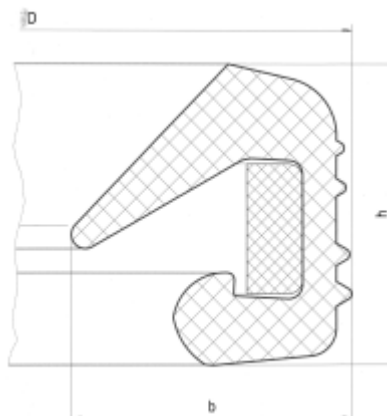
Уплотнительного кольца двухлепесткового типа
